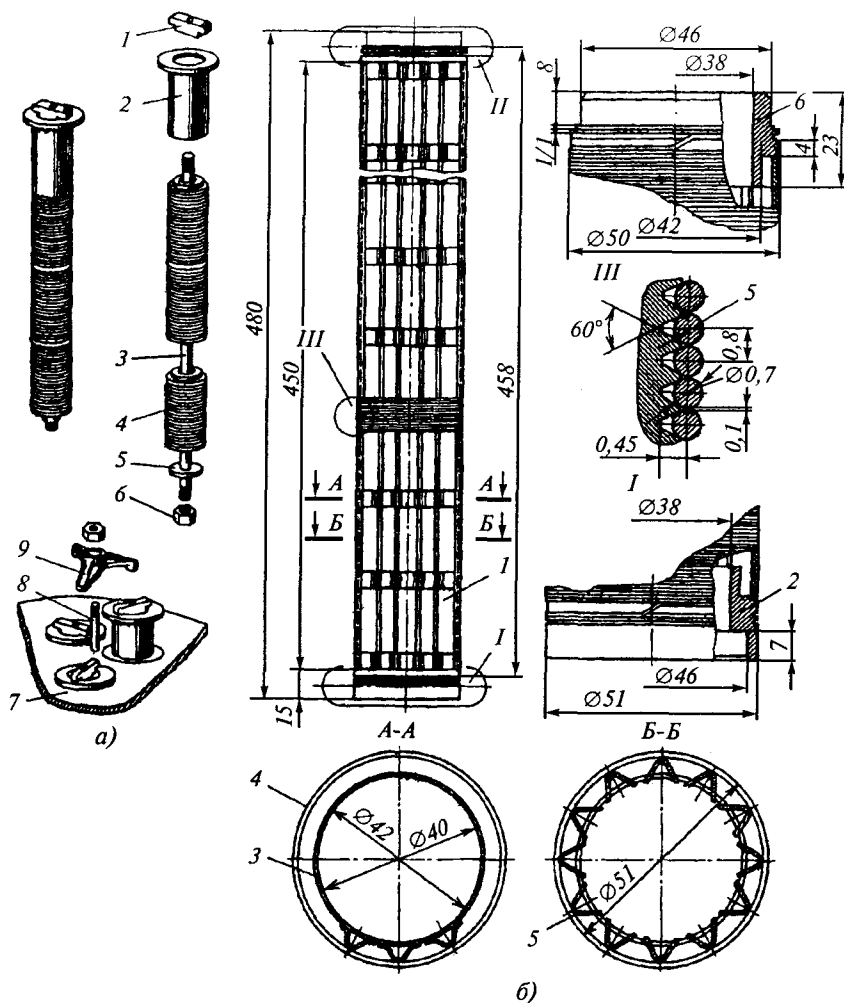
Патрон с проволочной опорной поверхностью:
